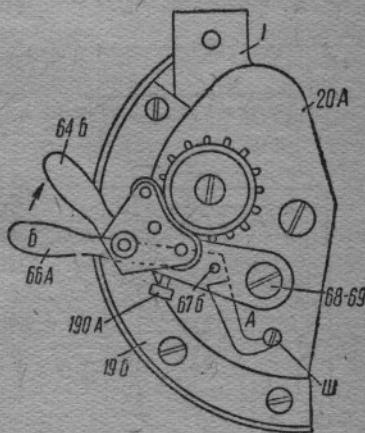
Схема роликовой каретки среднего (скачкового) барабана
